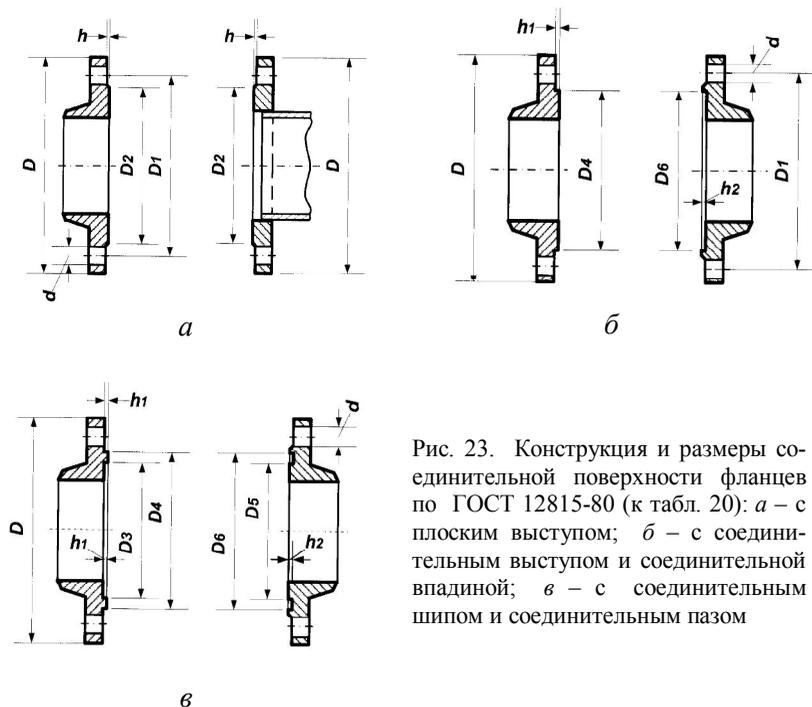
Конструкция и размеры соединительной поверхности фланцев по ГОСТ 12815-80 (к табл. 20): а – с плоским выступом; б – с соединительным выступом и соединительной впадиной; в – с соединительным шипом и соединительным пазом
